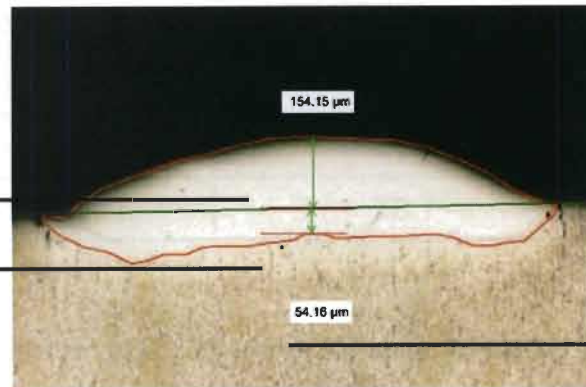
18 Cordón de soldadura #3 visto a 5X
